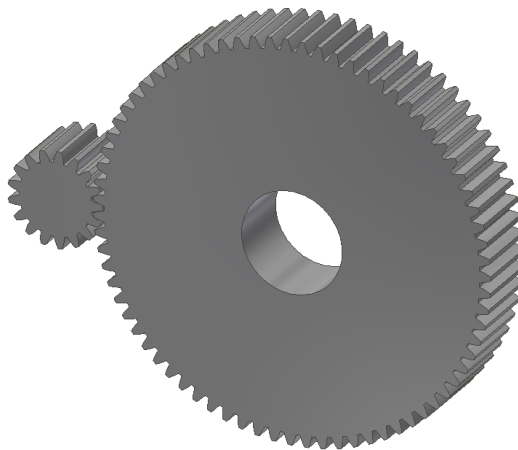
Зубчатий вінець тягового редуктора тепловоза
